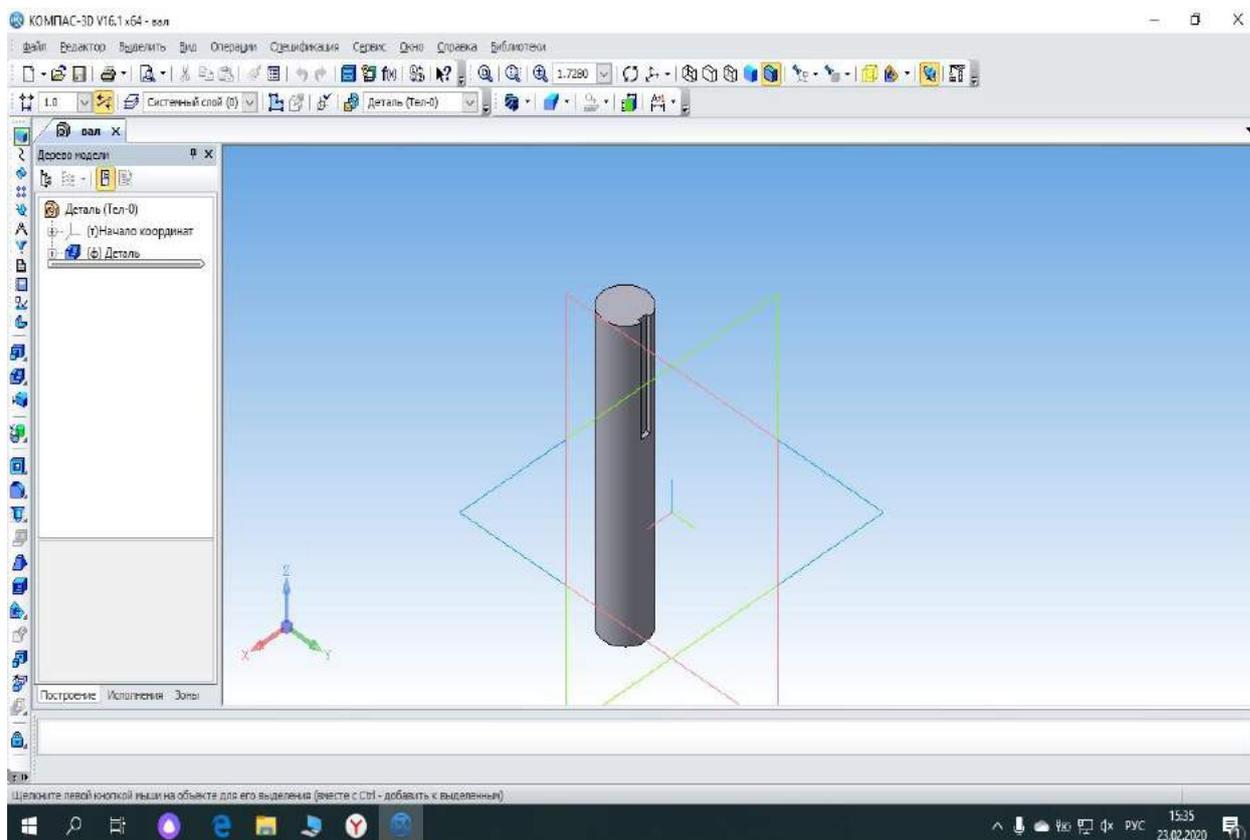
Скриншот детали «Вал» в3D – детализовке
